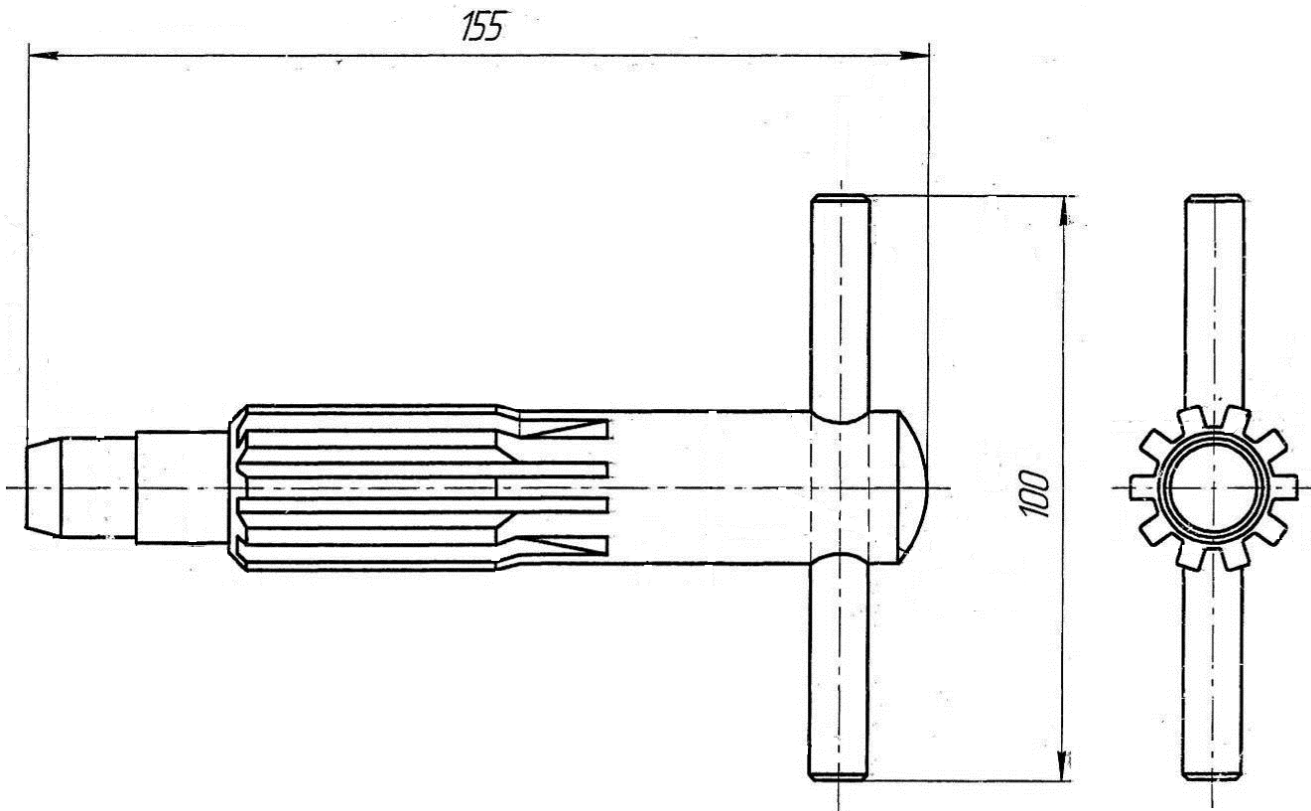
3M 7853-4023, Werkzeug zum Zentrieren der Kupplungsscheibe
